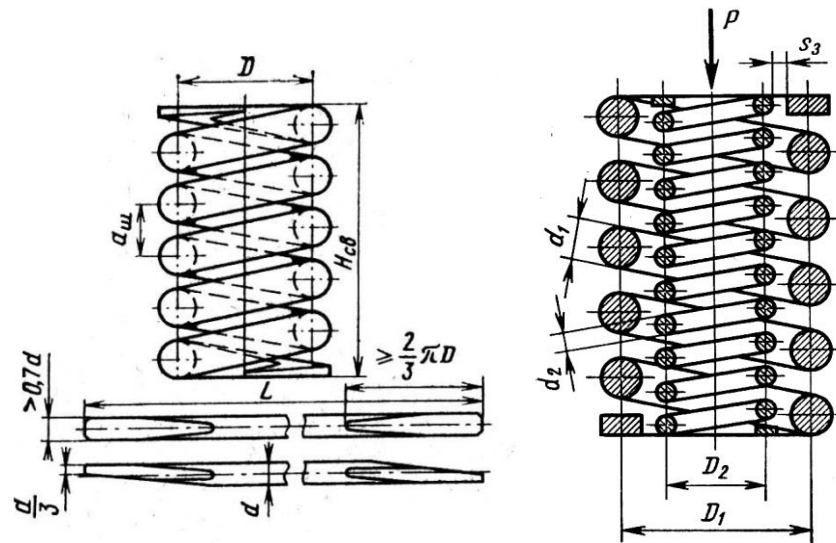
Розрахункова схема ресорного підвішування візка.
